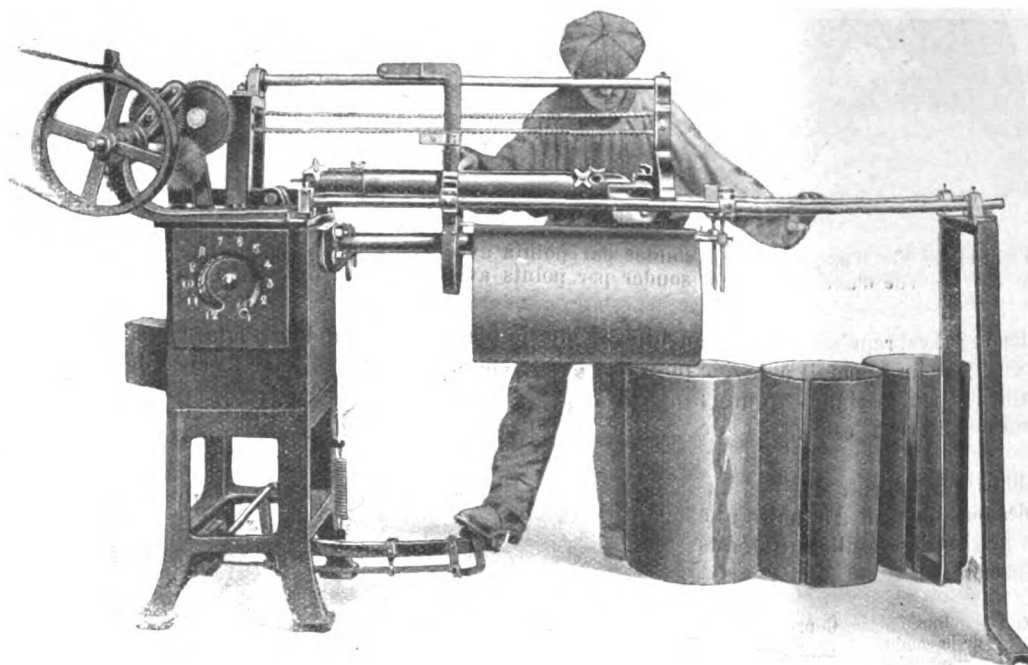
Vue d'une machine à souder continue (La Soudure électrique).
